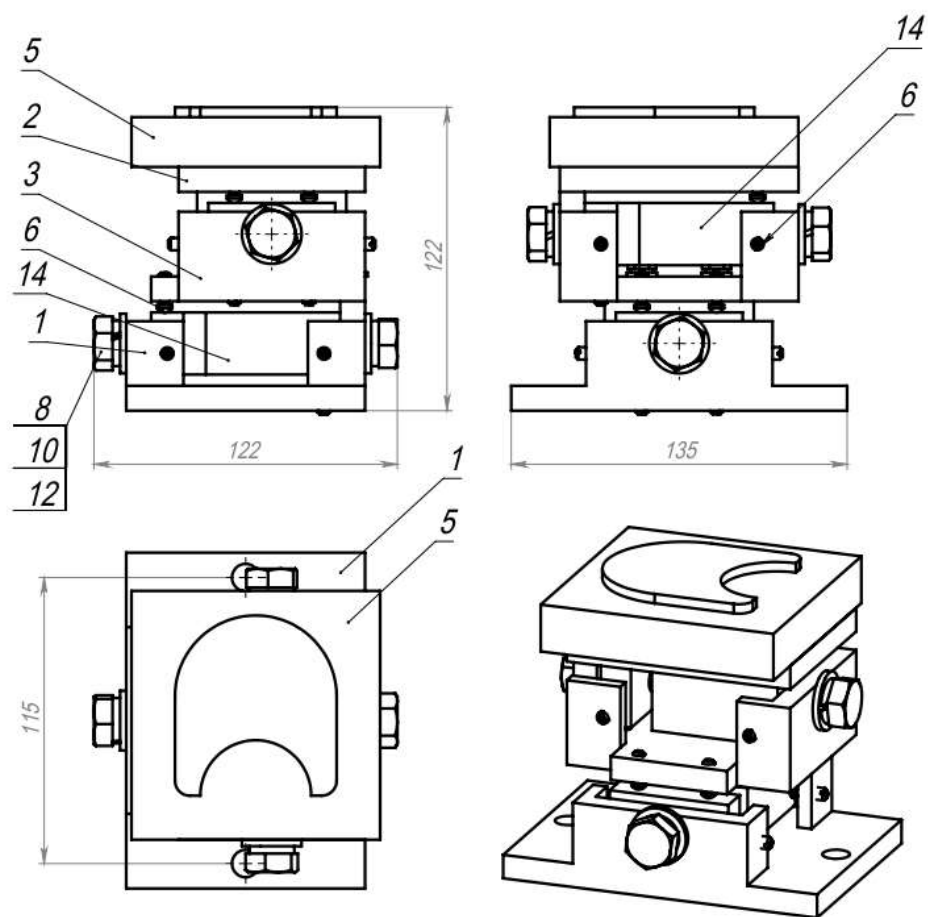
Пристій для вимірювання частоти коливань і сили різання при фрезеруванні
